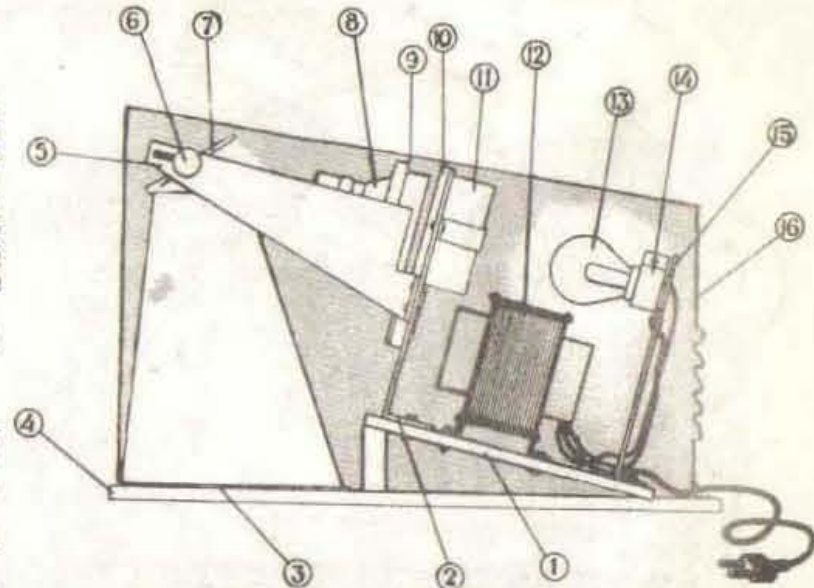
Secțiune printr-un diaproiector: 1 — panou de susținere a sistemului electric și optic; 2 — placă frontală de susținere; 3 — ecran; 4 — placă de postament; 5 — brațe de susținere a oglinzii; 6 — axul de fixare a oglinzii; 7 — oglindă; 8 — obiectiv; 9 — colier de susținere a obiectivului; 10 — loc pentru diapozitiv; 11 — susținerea condensatorului; 12 — transformator; 13 — bec; 14 — colier de susținere a becului; 15 — placa de susținere a becului; 16 — carcasa.
